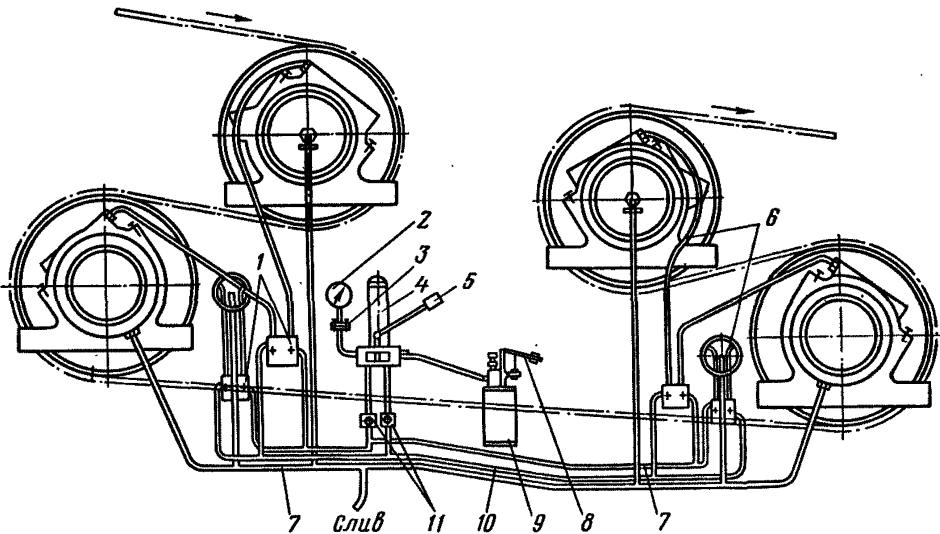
Устройство для густой смазки подшипников барабанов приводной станции конвейера 2ЛУ120
